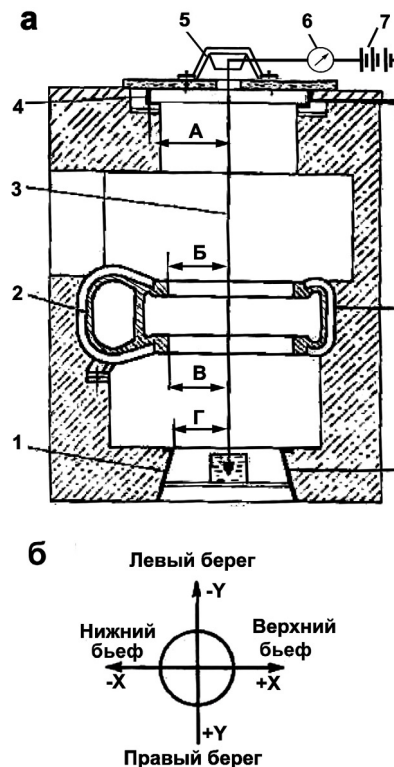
Схема центровки корпуса центробежного насоса:
